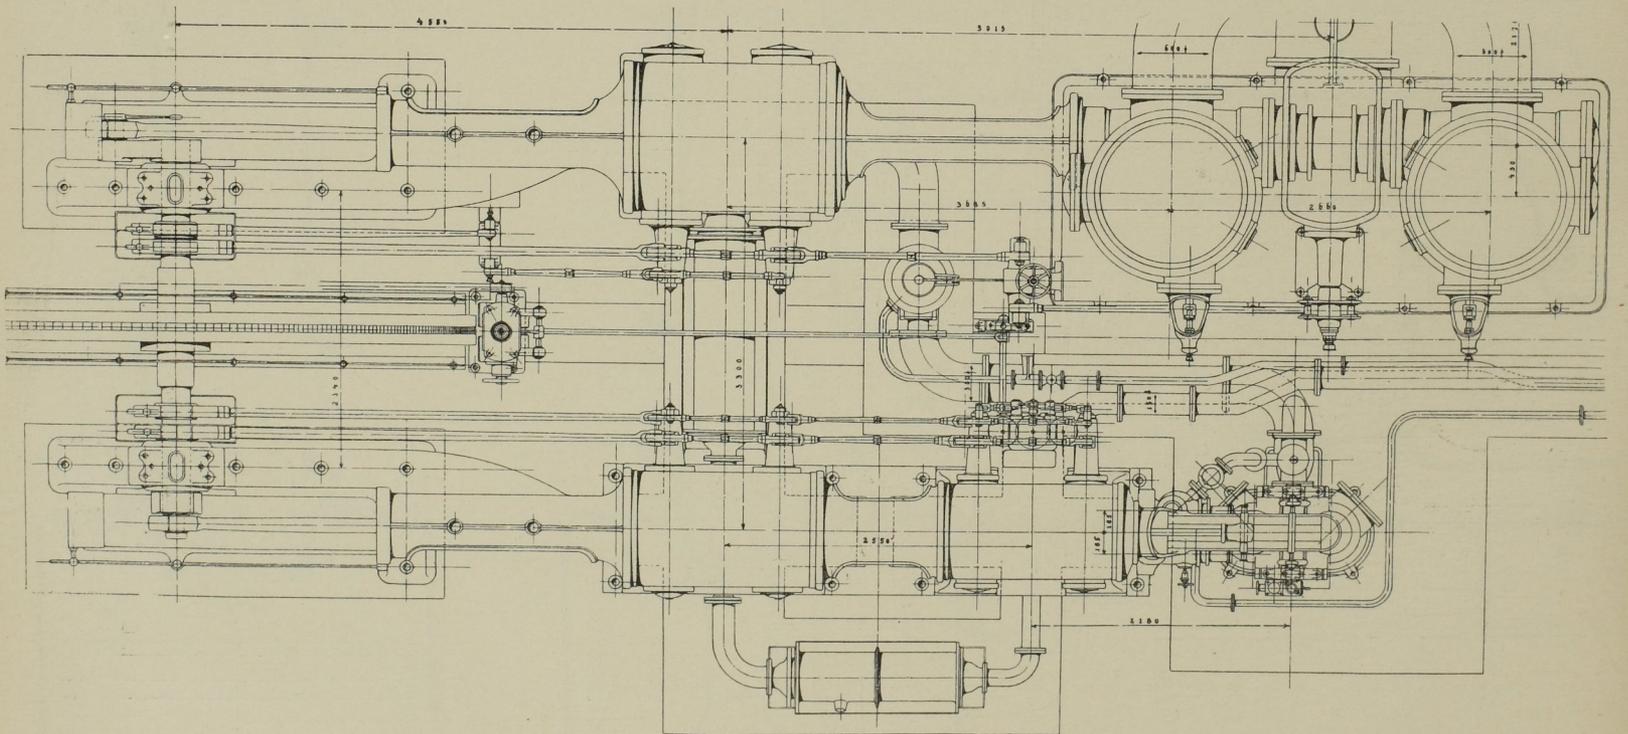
Grundriss der Pumpmaschine. Massst. 1:60.
